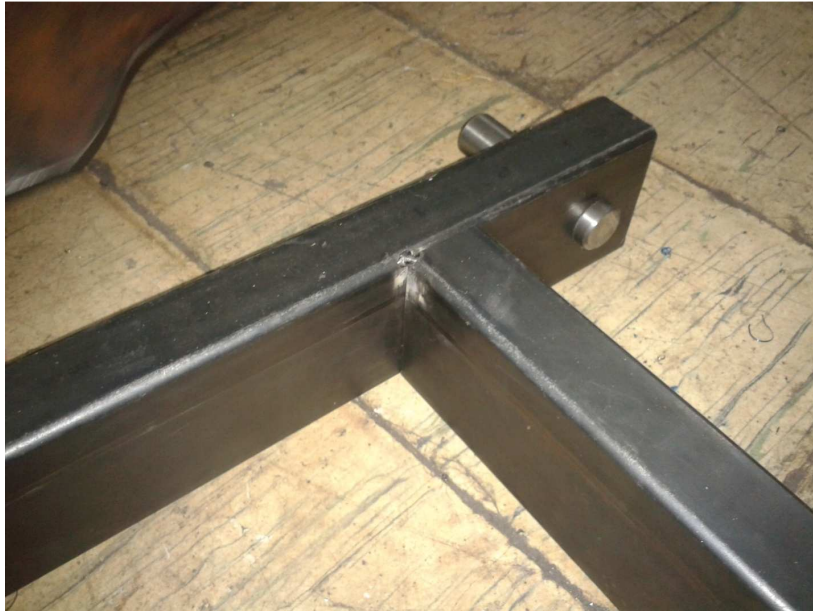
Soldadura entre tubos rectangulares y eje para chumaceras de pared
